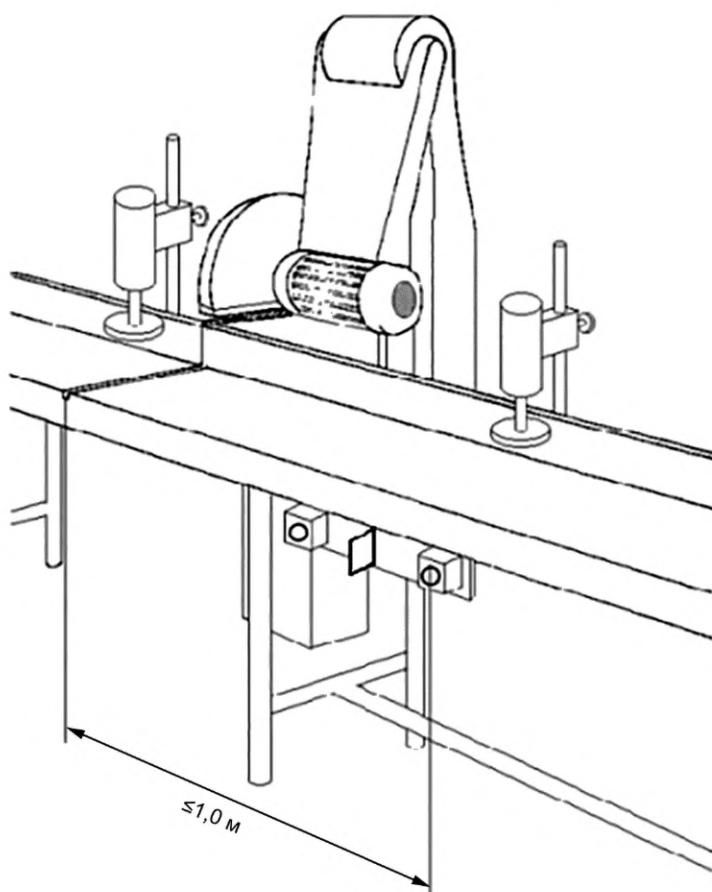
Расположение двуручного устройства управления на полуавтоматических станках
